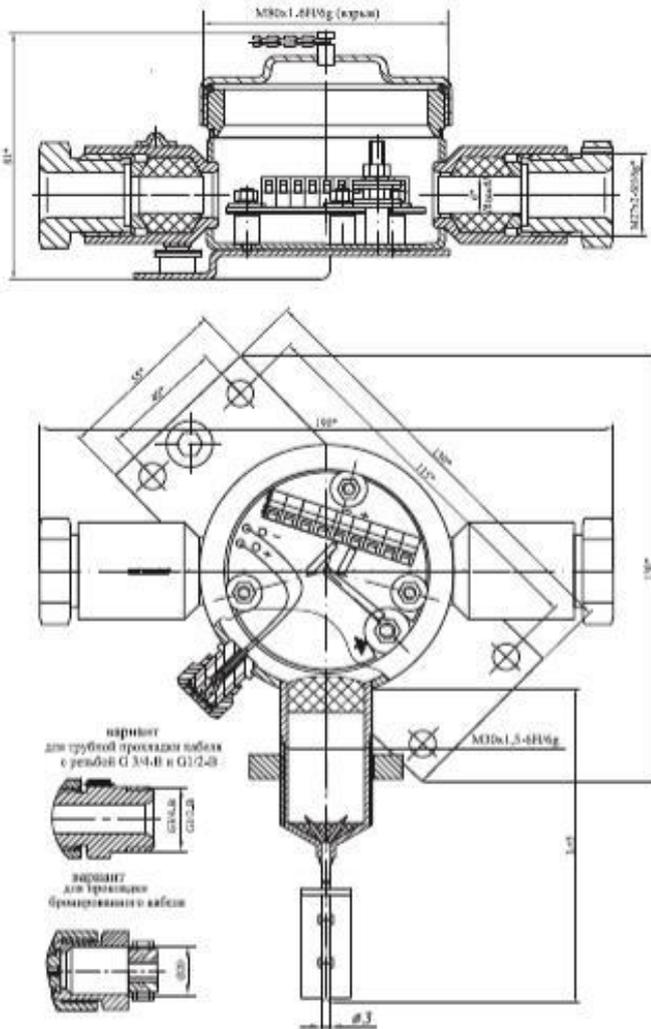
Извещатель пожарный ИП-102-1В-НС, монтаж на стену, вариант для открытой прокладки кабеля (К).
